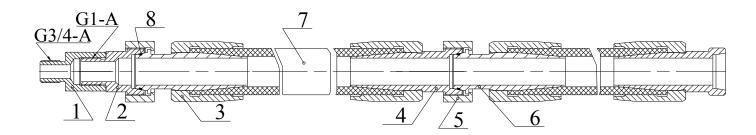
Шланг 1, 2 — муфта; 3, 5 — гайка; 4, 6 — корпус; 7 — рукав; 8 — кольцо
